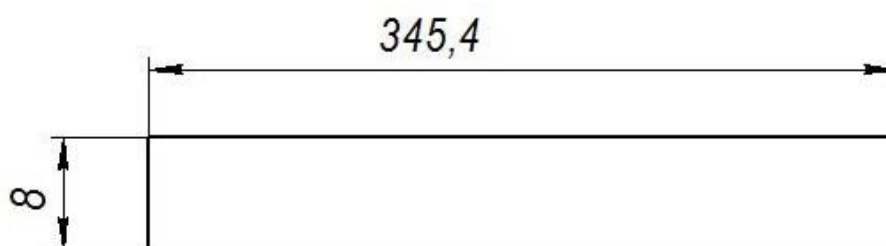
Эскиз обрабатываемой поверхности чистовым фрезерованием.
